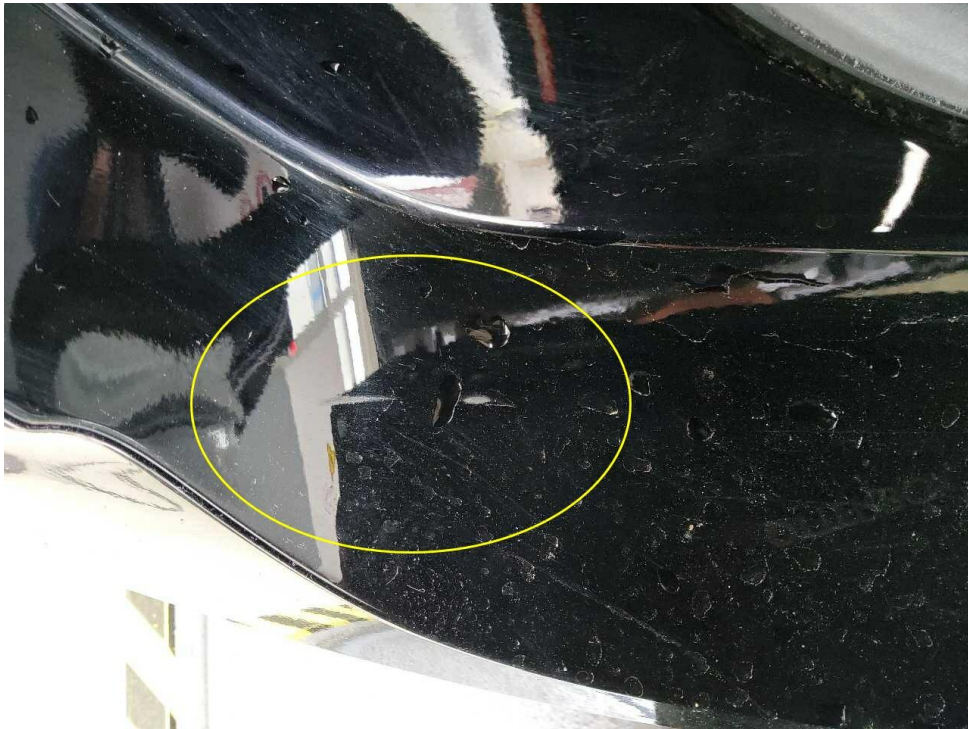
Stoßfänger hinten Ladekante verschrammt
